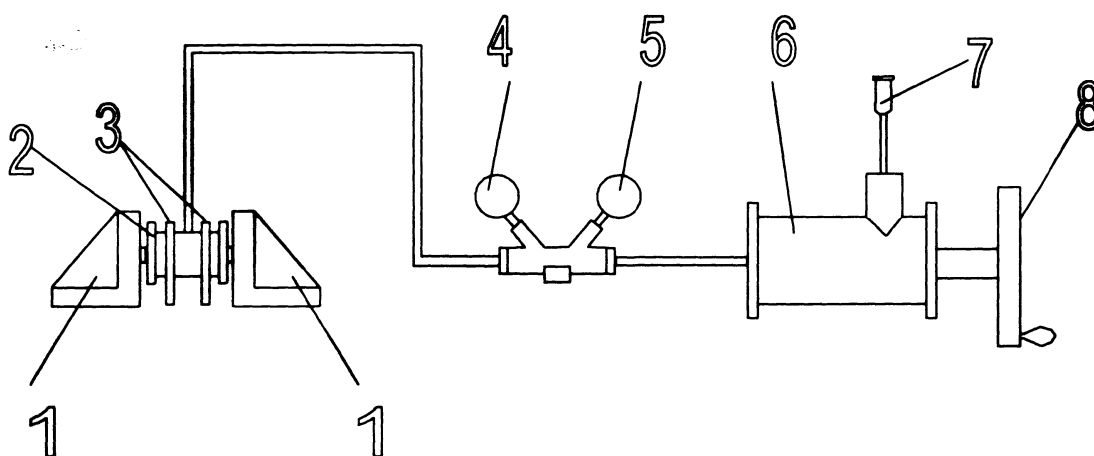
Схема проверки тормозных цилиндров задних колёс:
